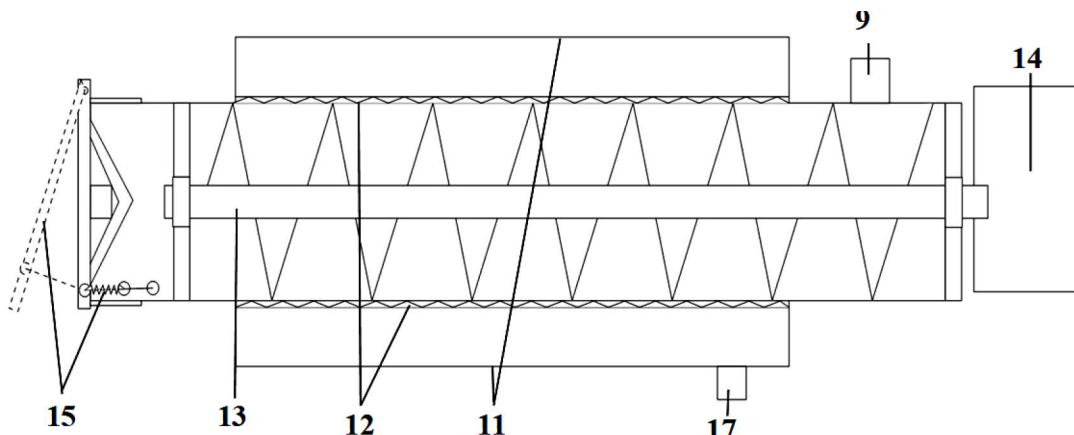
Система пресс-отделителя (вид сбоку в разрезе): 9 – рукав загрузки; 11 – статичный внешний корпус; 12 – внутренний перфорированный корпус; 13 – шнек для отжима; 14 – электродвигатель; 15 – отверстие с крышкой на пружине для выхода твердой фракции; 17 – отводящая труба /
